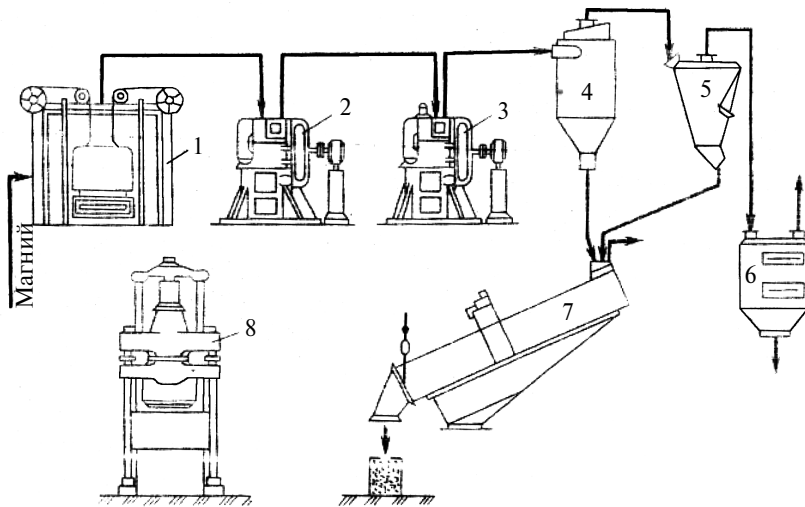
Аппаратурно-технологическая схема производства магниевых порошков фрезерованием: 1 – плавильная печь для литья заготовок; 2, 3 – фрезерные станки; 4 – циклон; 5 – сепаратор; 6 – масляный фильтр; 7 – вибрационный грохот; 8 – гидравлический пресс для брикетирования отходов
